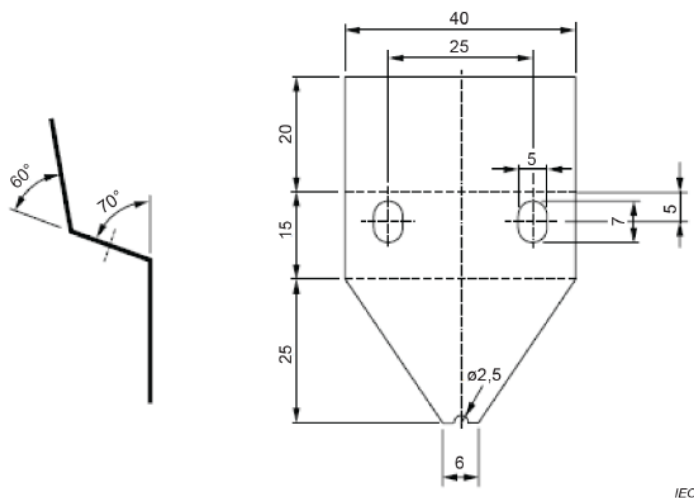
Dimensiones electrodo superior (IEC 60587)
